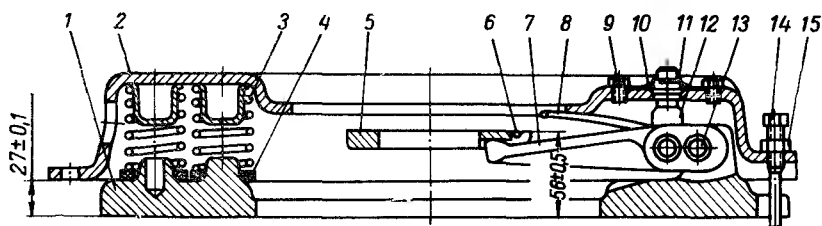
Нажимный диск сцепления с кожухом в сборе
